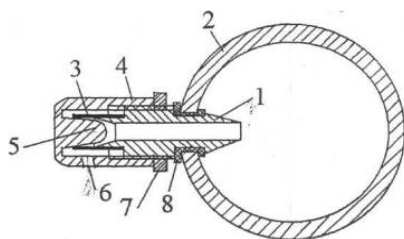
Капельница (1-штуцер; 2-поливной трубопровод; 3-резиновая трубка; 4-крышка; 5-конусообразный выступ; 6-отверстия; 7- контргайка; 8-прокладка)
